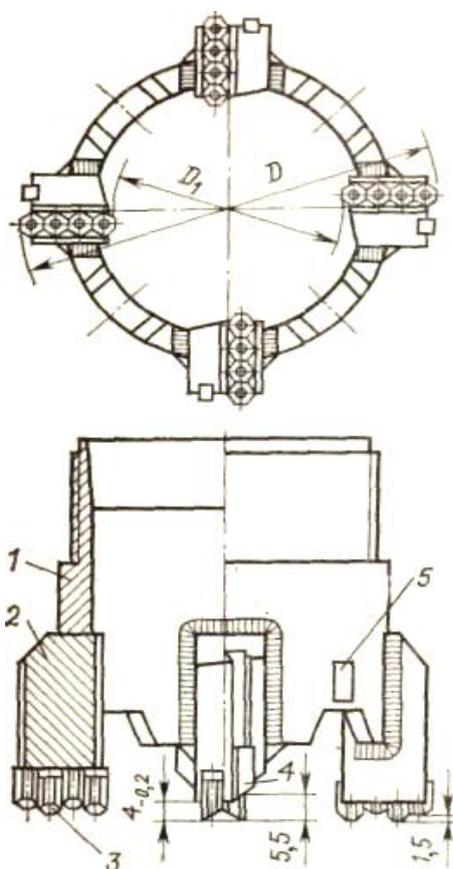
Ребристая коронка М-5: 1-корпус коронки, 2- ребро, 3 – основной резец, 4 – подрезной резец, 5 – место маркировки.
